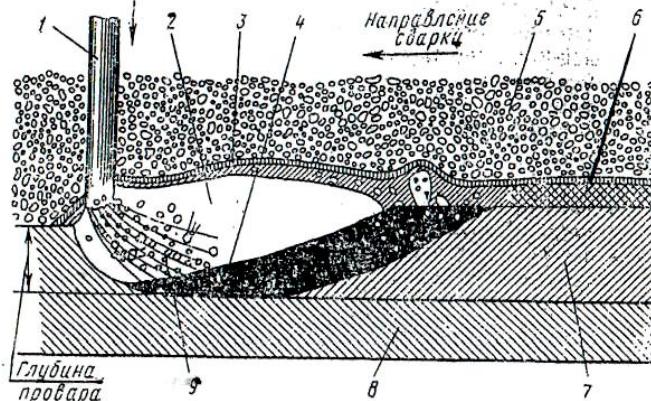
Схема горения сварочной дуги под флюсом
